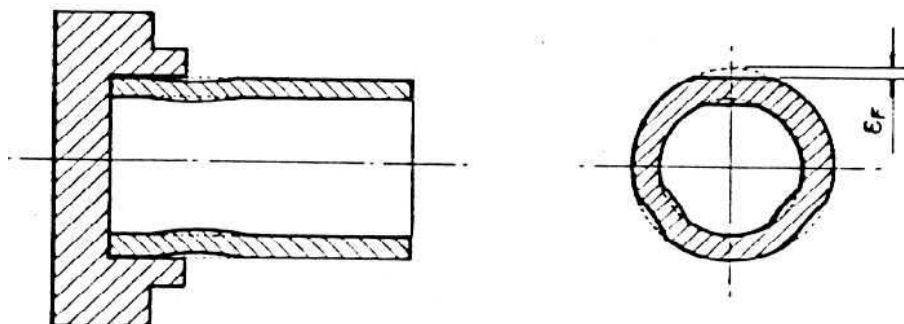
Desvio de fixação na usinagem de uma peça de parede fina por deformação. (FERRARESI, 1970)
